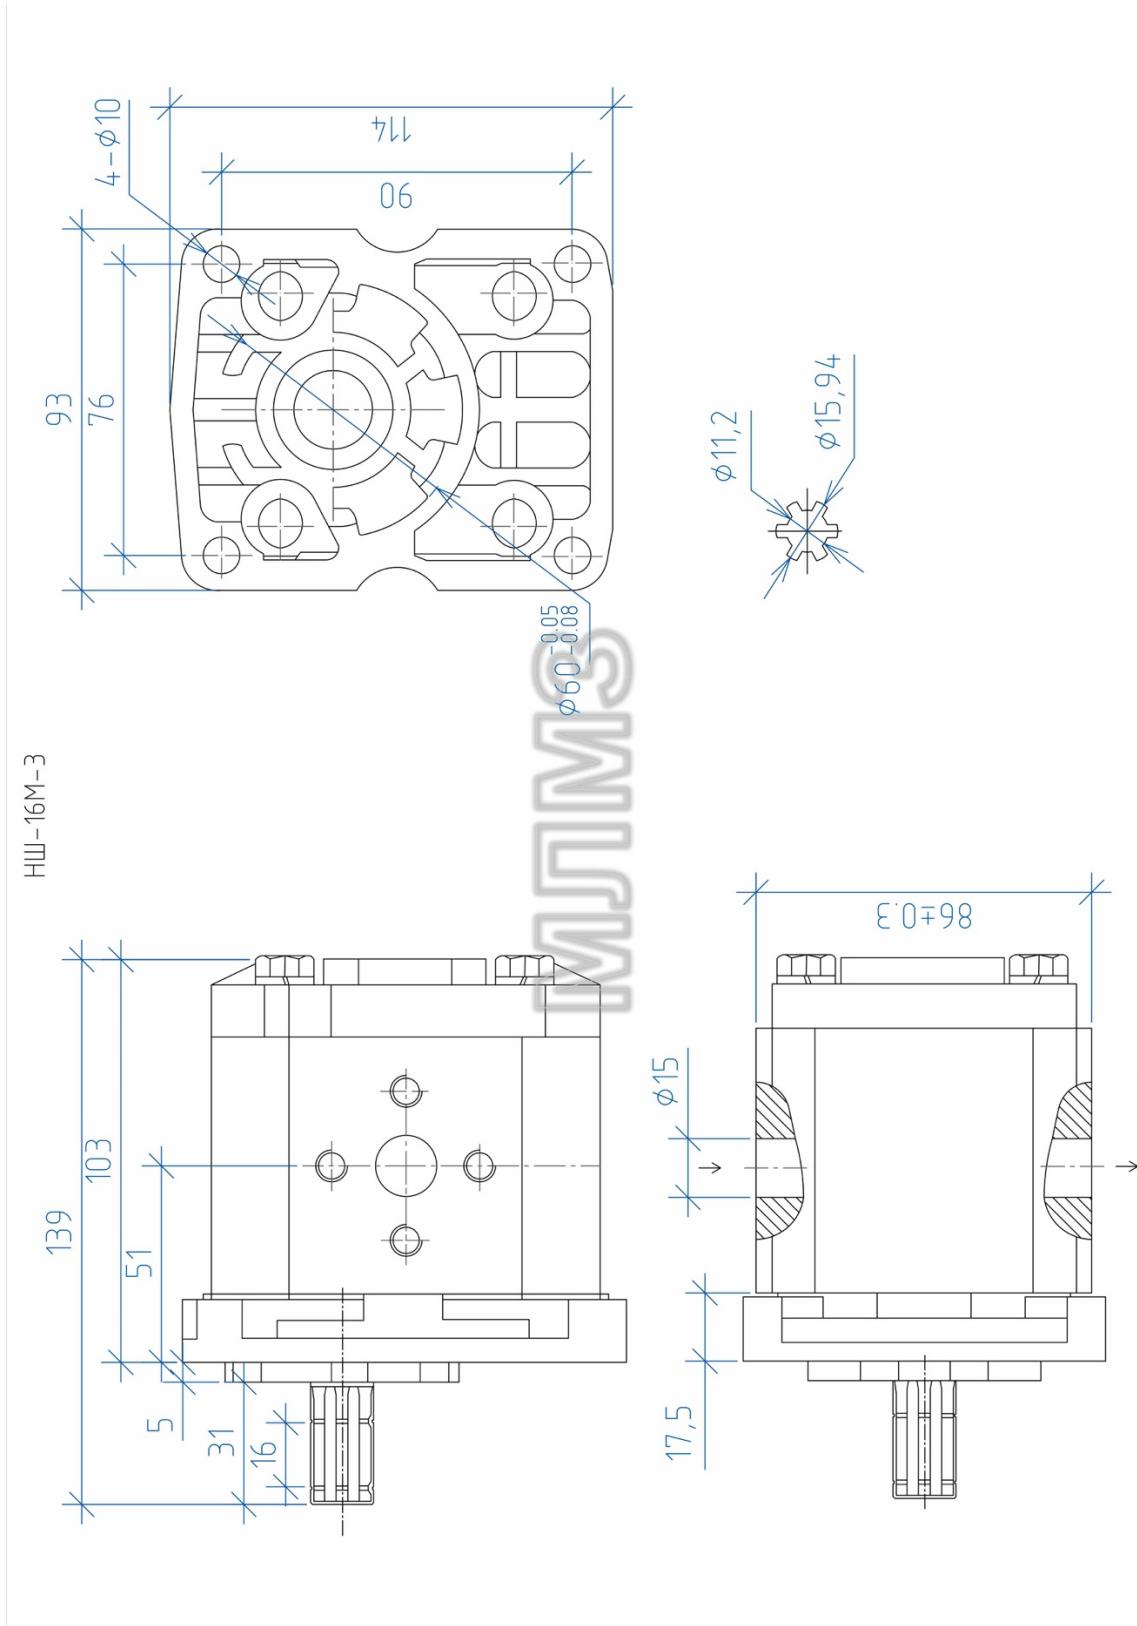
Насосы шестеренные НШ16М-3, НШ16М-3Л. Габаритные и присоединительные размеры.
